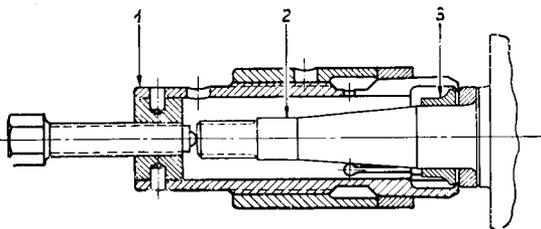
Inneren Laufring des inneren Radlagers abziehen
